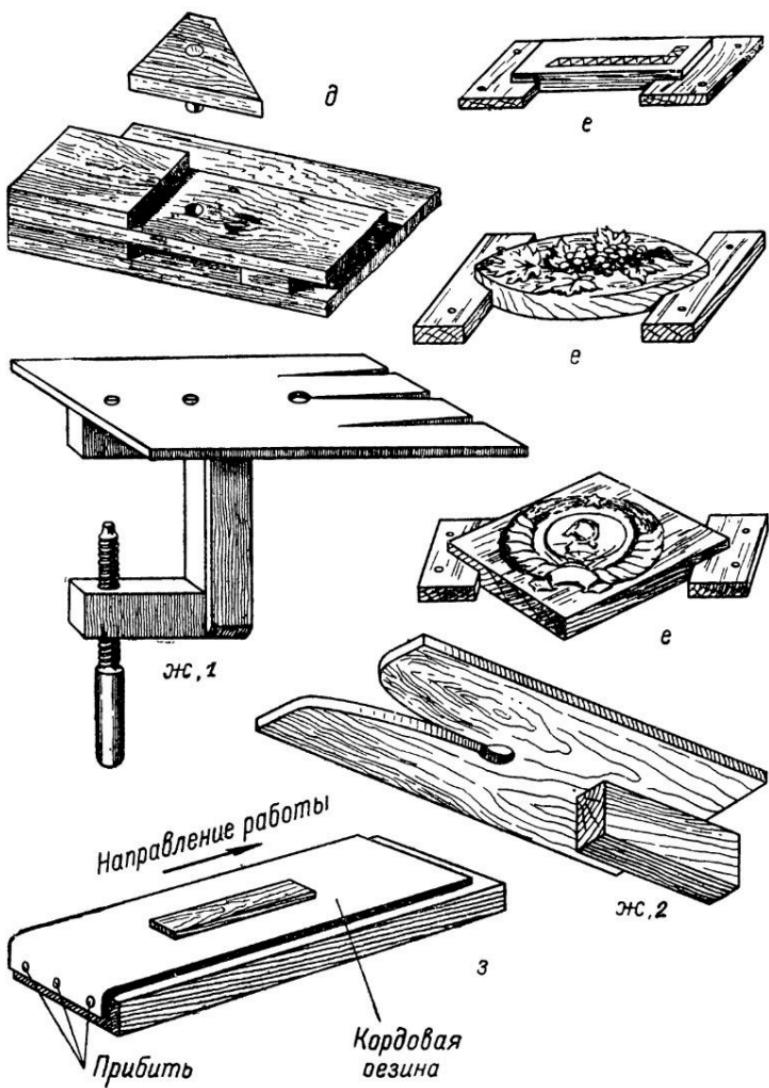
(продолжение). д — донце; е — державки для резьбы; ж — выпиловочные столики: 1 — со струбциной; 2 — для закрепления в задних тисках верстака; 3 — приспособления для строжки очень тонких дощечек и реек.
